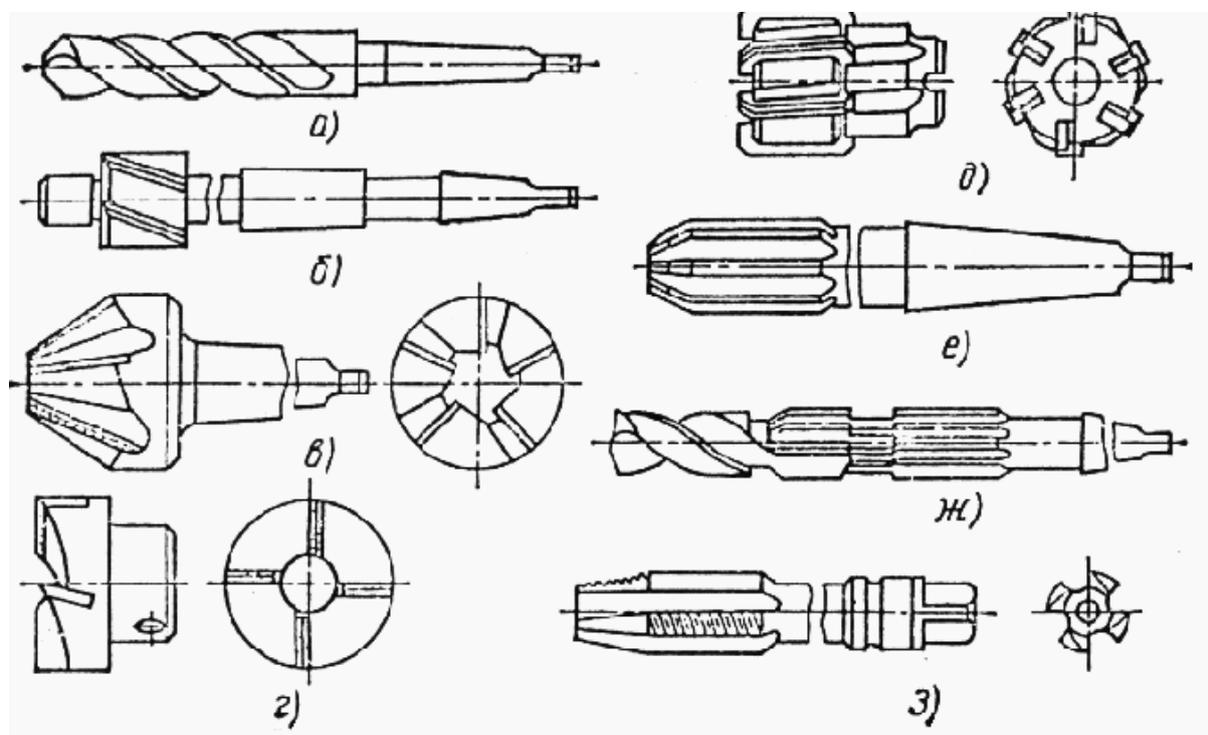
Режущие инструменты, применяемые на сверлильных станках
